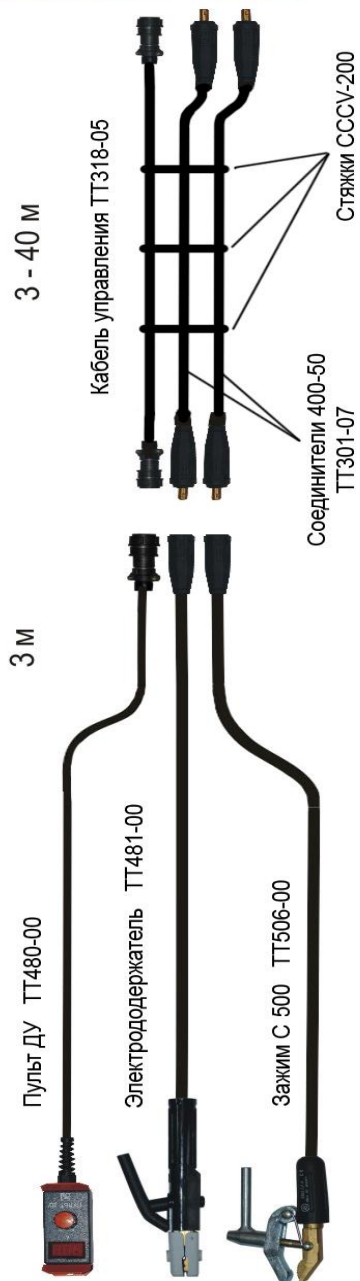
Схема подключения источника ДС400.33М при сварке в режиме РД с соединителями
